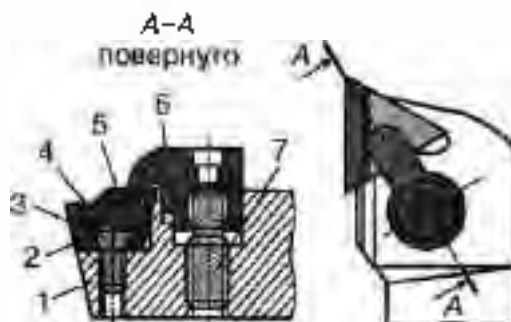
РІЗЕЦЬ З КРІПЛЕННЯМ БАГАТОКРОМКОВОЇ ПЛАСТИНКИ З ТВЕРДОГО СПЛАВУ ПРИХВАТОМ — КОСТИЛЕМ
